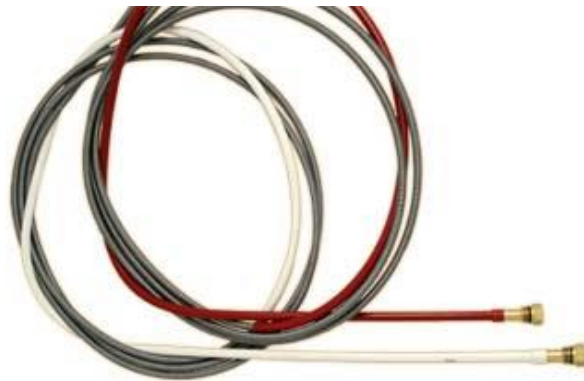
Conducto guía del hilo de soldadura para mover el hilo desde el alimentador hasta el cabezal de la máquina. Fuente: [37].
